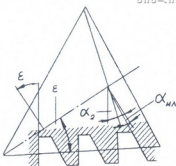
Осевой пилообразный профиль червячной фрезы
